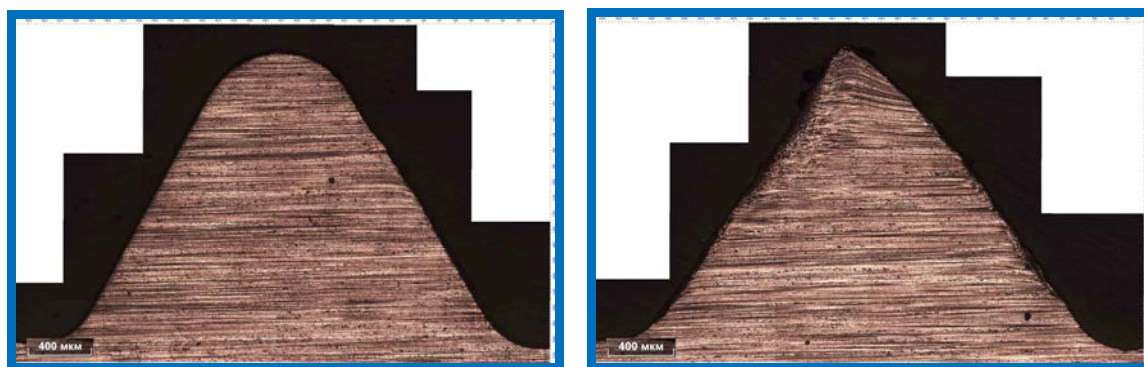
Вид профиля резьбы, покрытой КСИЛАНом, до (а) и после (б) испытаний
